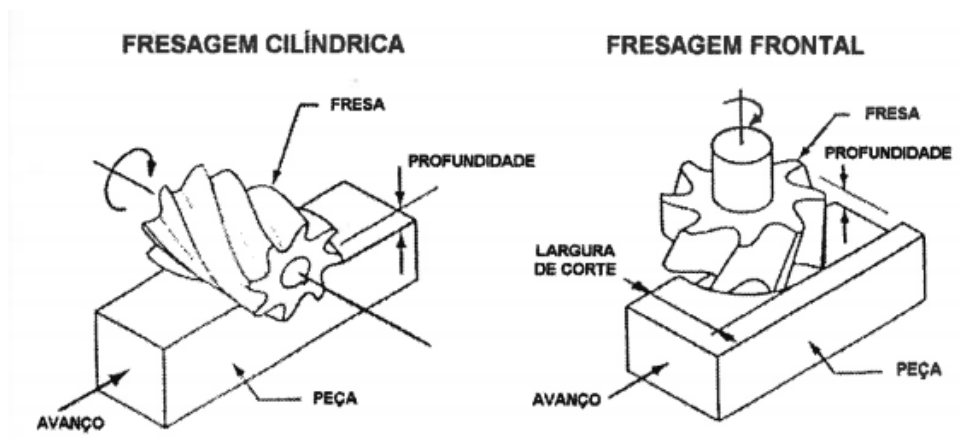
Fresagem cilíndrica e fresagem frontal [24].
